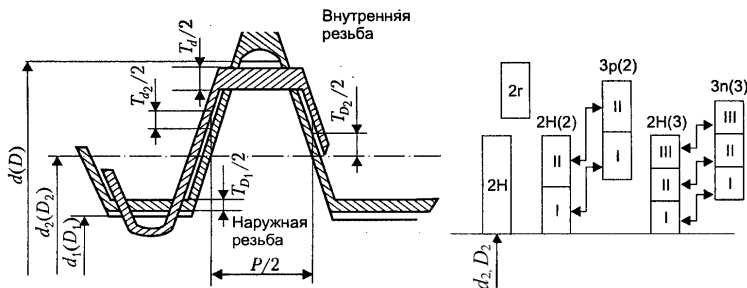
Расположение полей допусков резьбы с натягом
